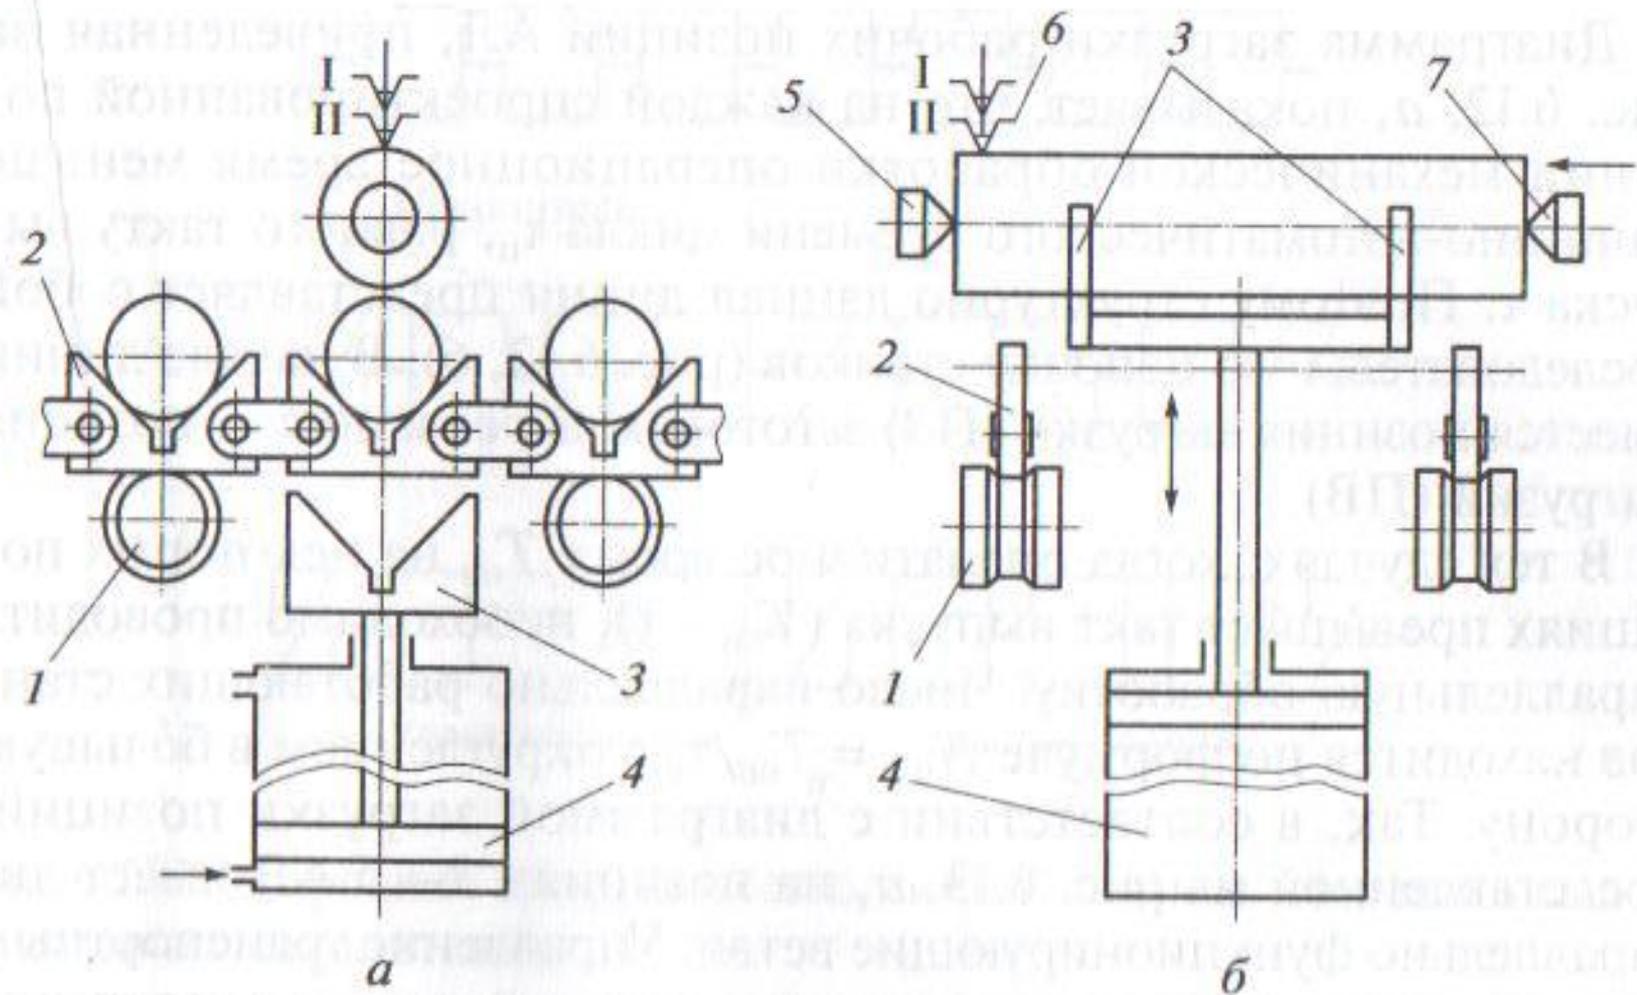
Схемы транспортирования (а) и установки цилиндрических заготовок на рабочие позиции (б)
